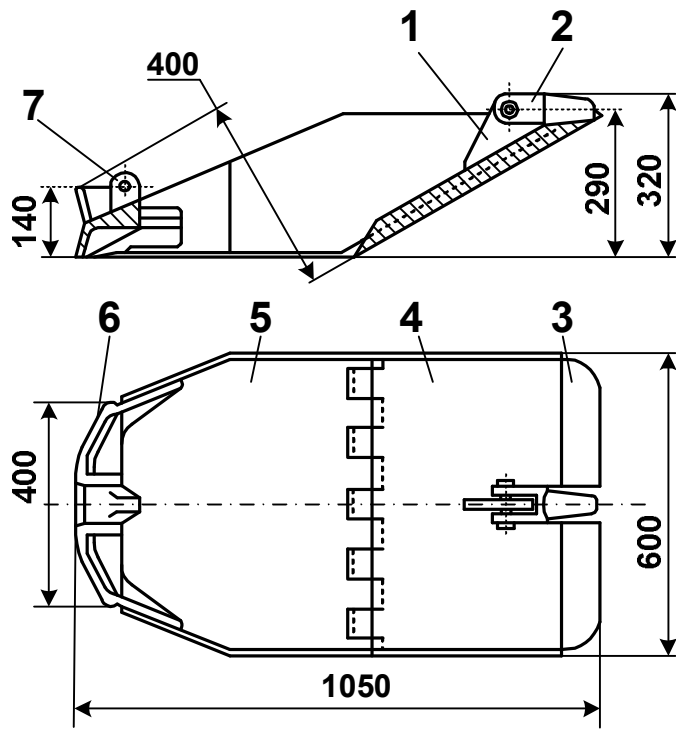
Совковый скрепер сварной конструкции со сплошным лезвием:
